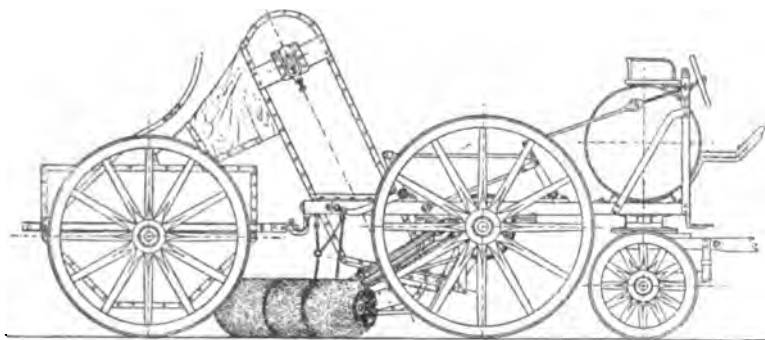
Strassenkehrmaschine „Salus“ mit Elevator.
